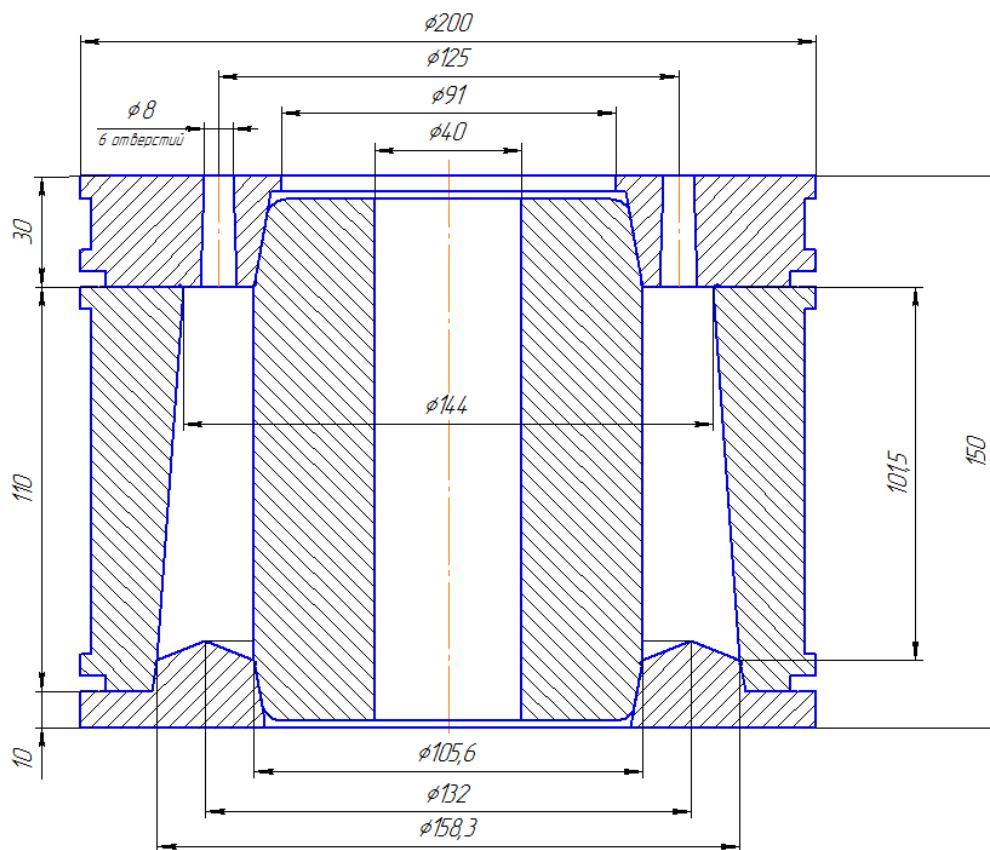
Пресс-форма манжеты Пакера в разрезе.
